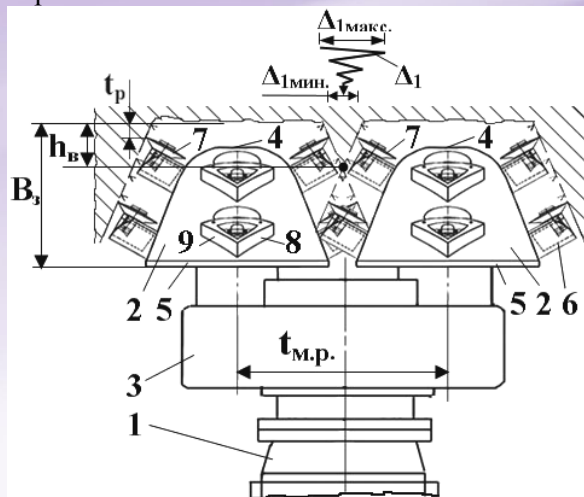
Двухкорончатый исполнительный орган реверсивного действия
